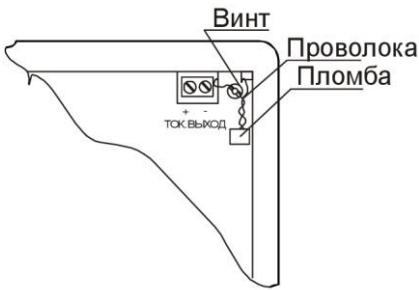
Схема пломбировки вторичного преобразователя при креплении в щит
